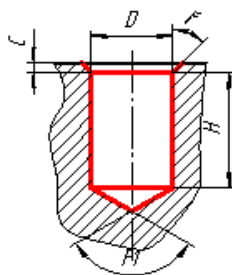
КТЭ цилиндрическое отверстие глухое с фаской для поверхностей №21, 22
